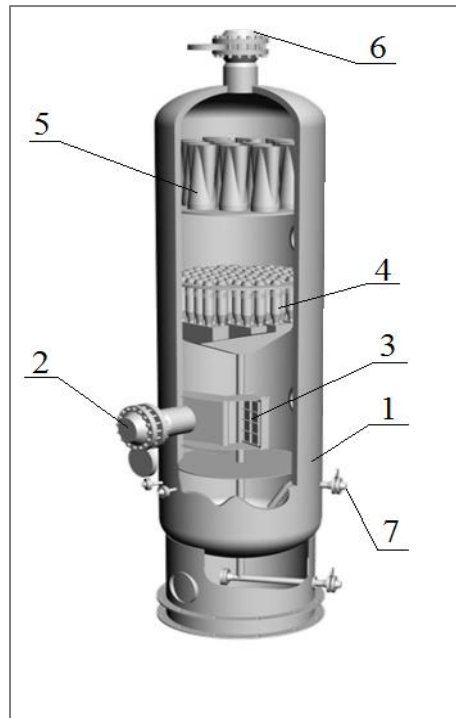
Сепаратор конструкции «Sulzer Chemtech»:
